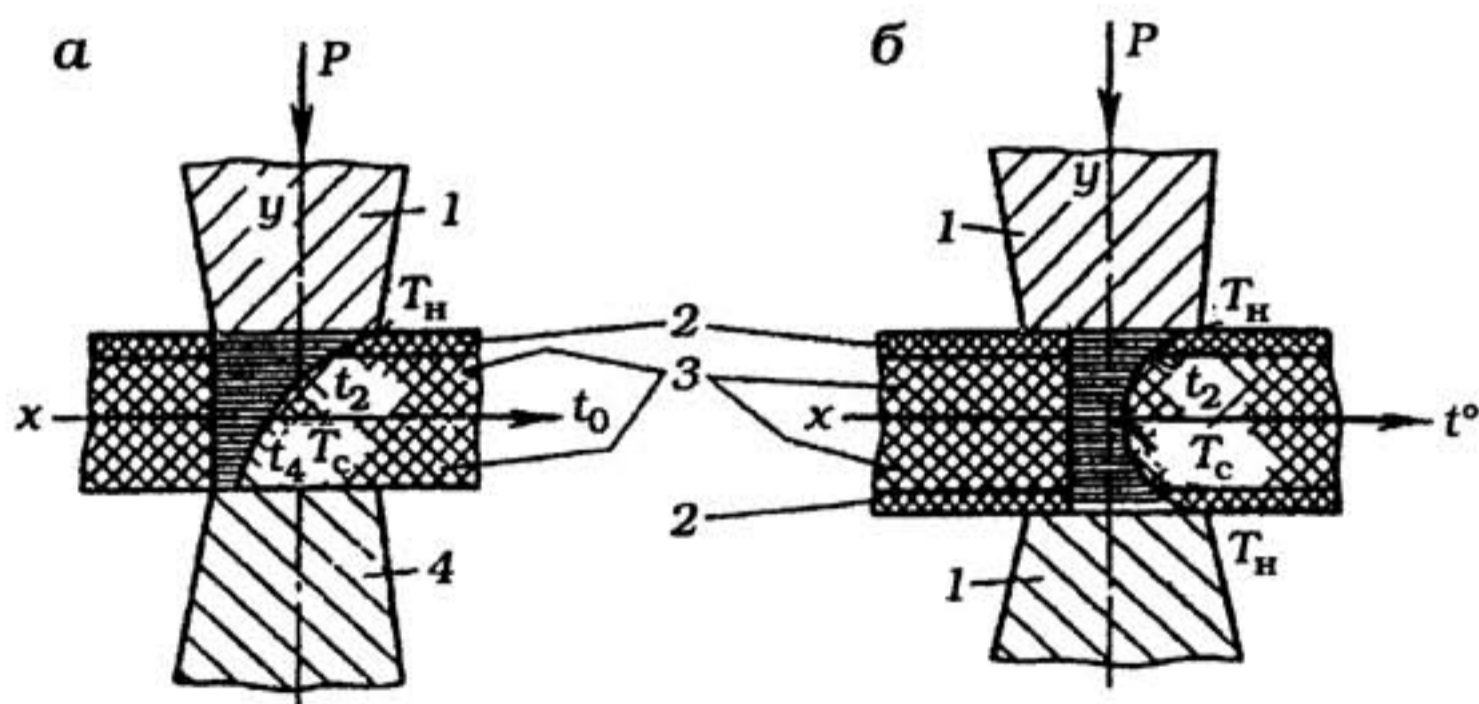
Схема контактно-тепловой сварки с односторонним (а) и двусторонним (б) нагревом: 1 — нагретый инструмент; 2 — прокладки; 3 — свариваемые материалы; 4 — холодный инструмент;  $T_H$  — температура нагретого инструмента;  $t_2$  — температура внешней поверхности изделия;  $T_C$  — температура свариваемых поверхностей;  $t_4$  — температура холодного инструмента
